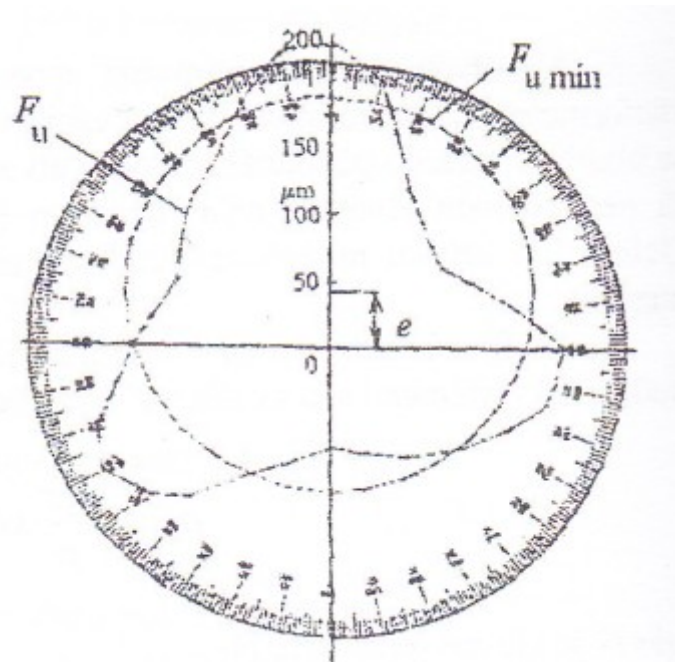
Konečný tvar obrobku po soustružení mezi hroty [1]
